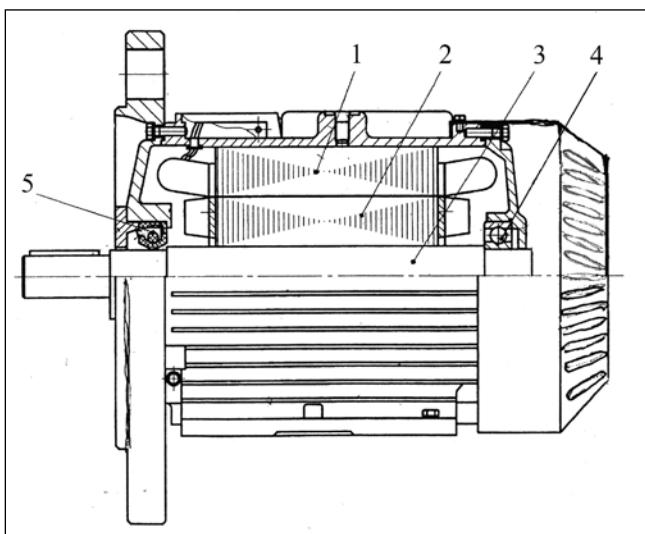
Электродвигатель с одним подшипником ротора: 1 — обмотка статора, 2 — ротор, 3 — вал ротора, 4 — подшипник, 5 — манжета
